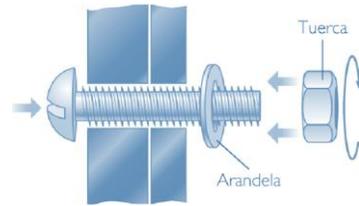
Tornillo- Tuerca Fuente: [38]
